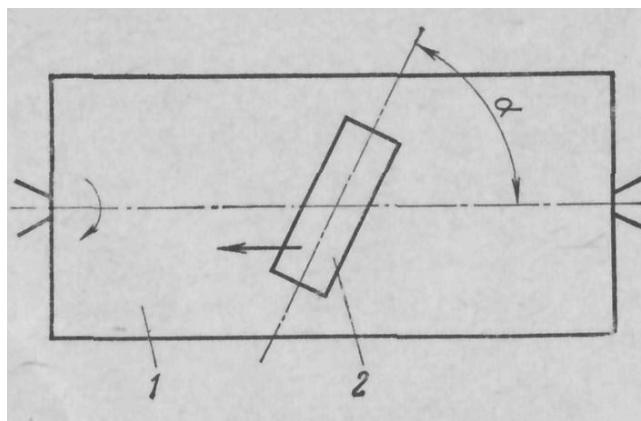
Схема обработки выглаживанием с угловой установкой инструмента: 1 – заготовка; 2 – цилиндрический выглаживатель [67].
